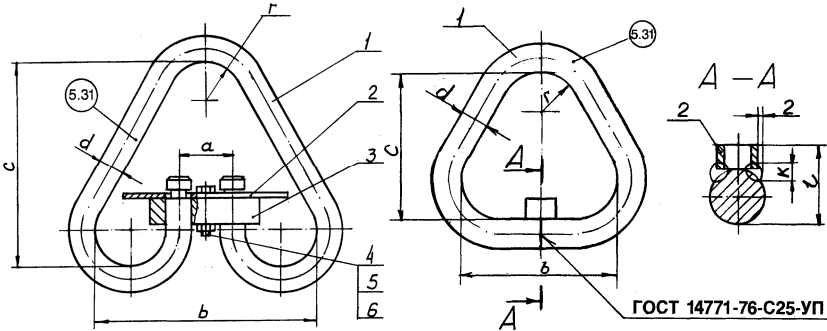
Ланка рознімна трикутна (Pt1): 1- скоба; 2 - обмежувач; 3 - планка; 4 - болт; 5 - гайка; 6 - шплінт
